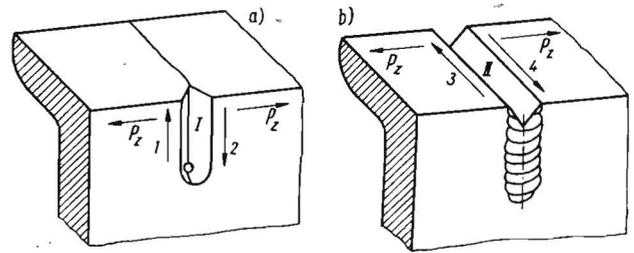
Günstige Schweißfolge: a) Aufnahme der Querschrumpfung durch den ungeschweißten Querschnitt; b) Aufnahme der Querschrumpfung durch den geschweißten Querschnitt
